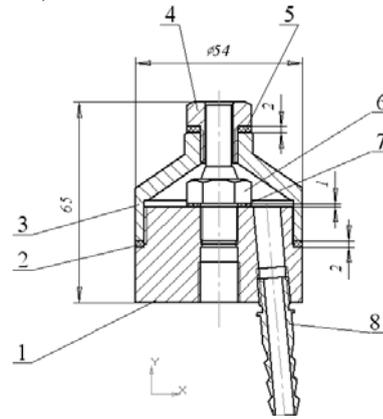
Схема форсунки: 1 – днище; 2, 5, 7 – прокладки; 3 – корпус; 4 – сменная головка корпуса; 6 – сменная головка днища; 8 – штуцер для подачи воды
